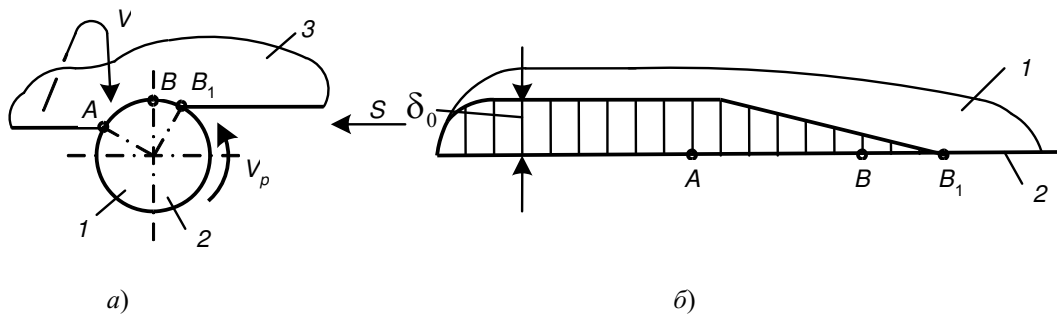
Схема работы (а) и вид износа режущей кромки (б) чашечного резца с непрерывным ее обновлением: 1 – режущий элемент; 2 – режущая кромка; 3 – заготовка;  $V$  – скорость резания, м/с;  $V_p$  – скорость перемещения РК, м/с;  $S$  – подача, мм/об;  $\delta_0$  – величина износа режущей кромки резца;  $B_1, A$  – точки входа и выхода режущей кромки из зоны резания;  $B$  – величина заглупления режущей кромки резца в заготовку
